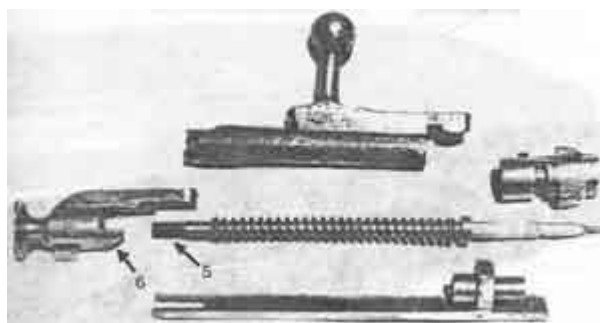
Разобранный затвор. Внимание: для обеспечения сборки затвора
